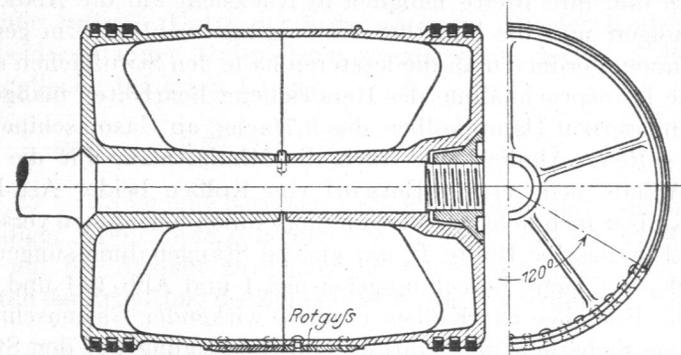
Gleichstromdampfmaschinenkolben nach Prof. Stumpf.
